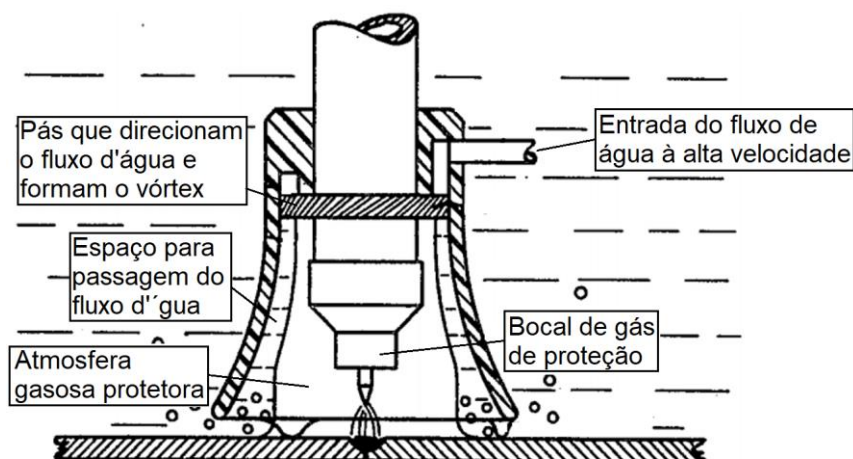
Dispositivo para Soldagem Subaquática – Patente Número 4172974.
